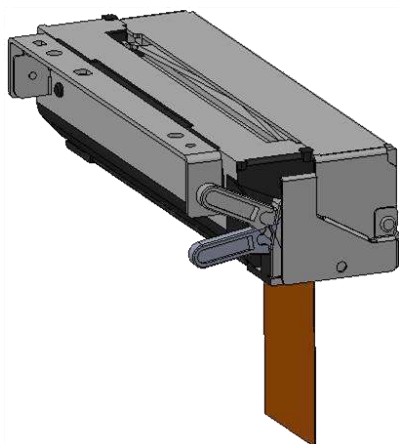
Устройство печати кассовых чеков SII CAPD347E-E
